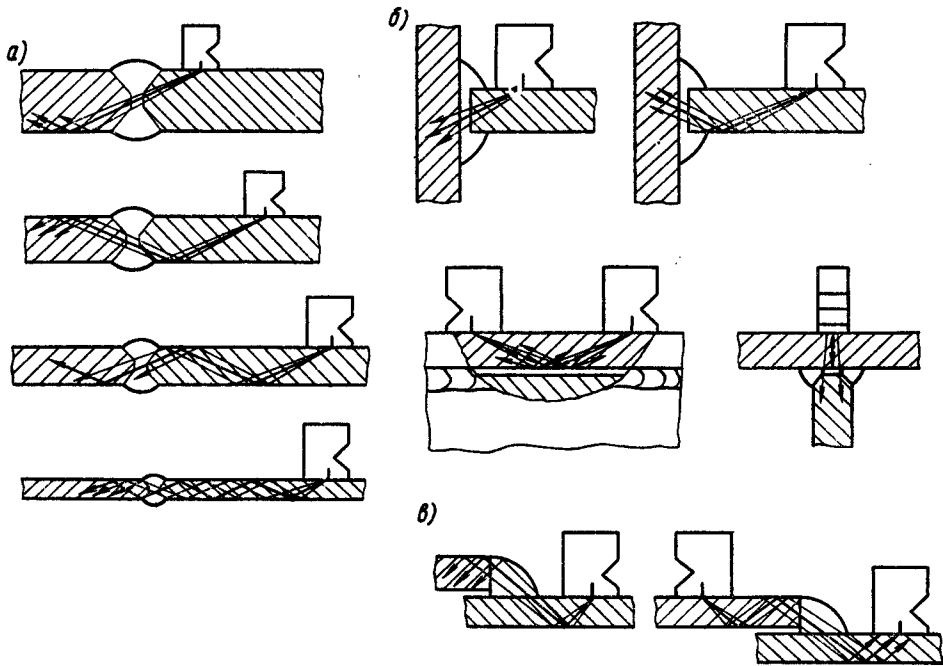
Схемы испытания швов сварных соединений
